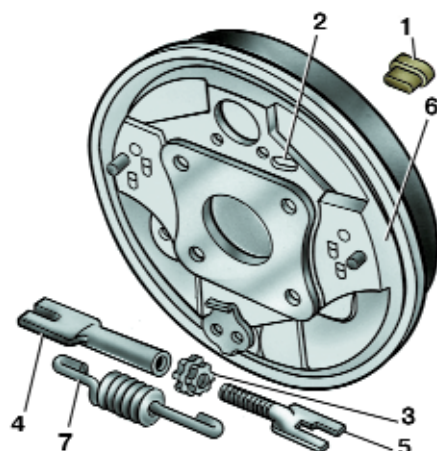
Детали привода стояночной тормозной системы: 1 – заглушка; 2 – отверстие для регулировки привода стояночной тормозной системы; 3 – гайка регулировочная; 4 и 5 – наконечники распорной планки; 6 – щит тормоза; 7 – стяжная пружина
